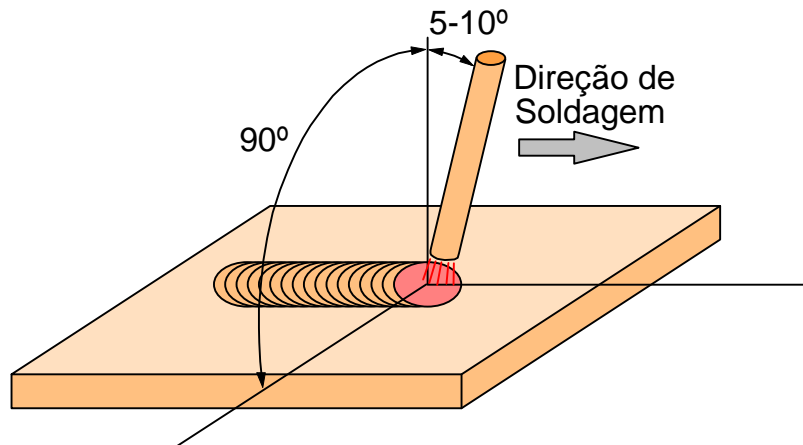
Posicionamento do eletrodo para a soldagem na posição plana.
